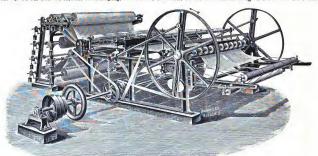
Papierothneidmaschine eon der Maschinenbauanstatt Goltern.
